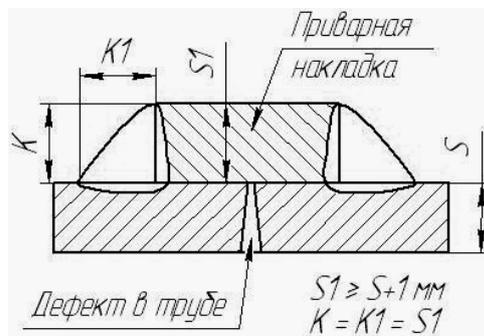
Конструкция нахлесточного сварного соединения при ремонте методом приварной накладки.
